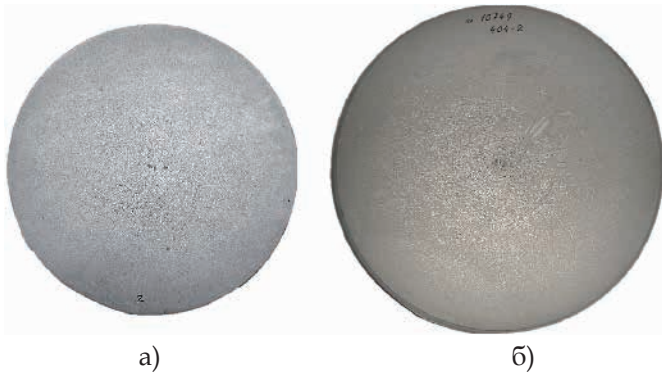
Макроструктура исследуемых осевых заготовок, изготовленных из различного непрерывнолитого металла:
